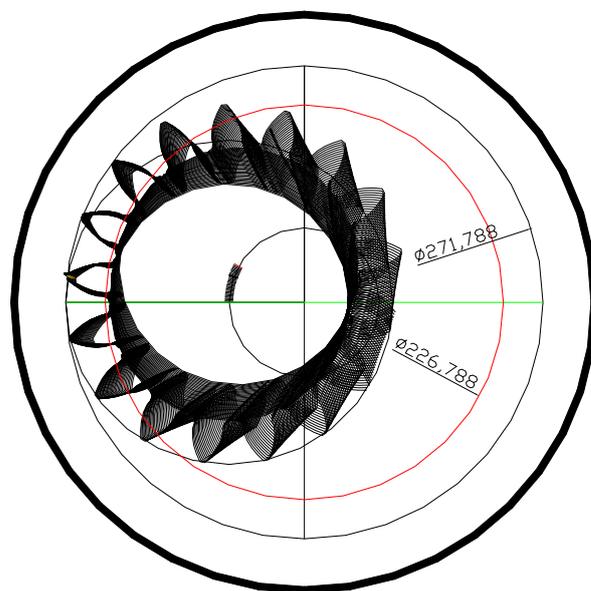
Положения долбяка в движении по отношению к неподвижной заготовке
